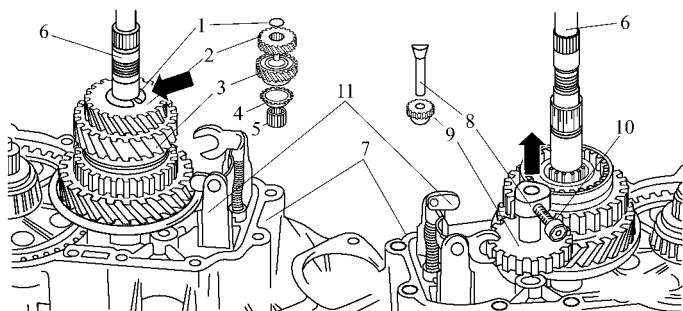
59 输出轴二档齿轮三档齿轮及倒档齿轮的拆卸
